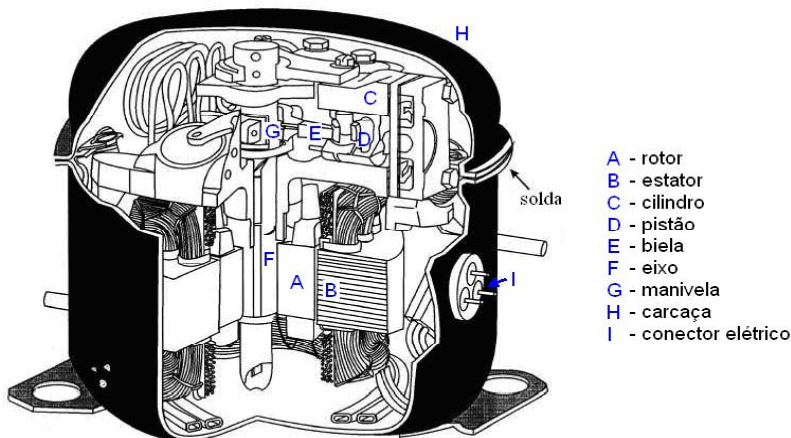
Vista em corte do compressor hermético de refrigeração.
